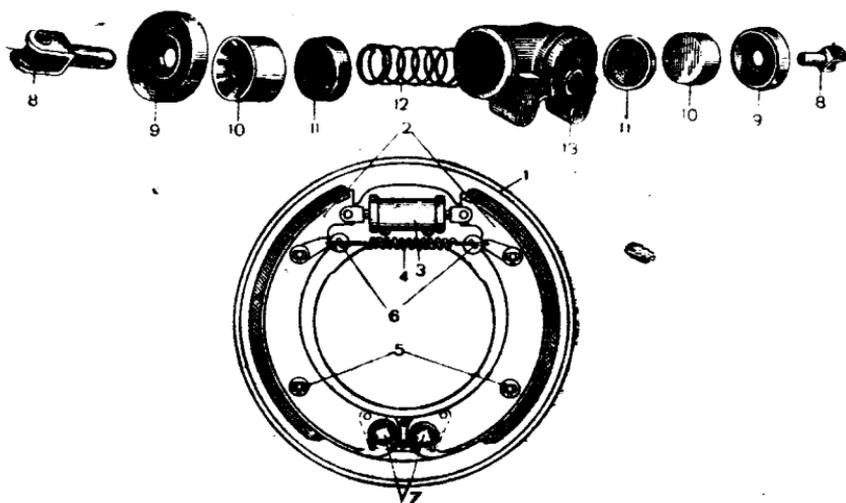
Схема установки тормозных колодок и детали тормоза цилиндра:
